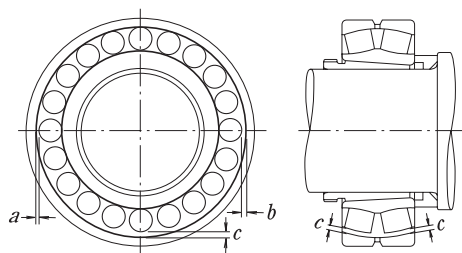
Измерение зазора в крупногабаритных сферических роликоподшипниках
